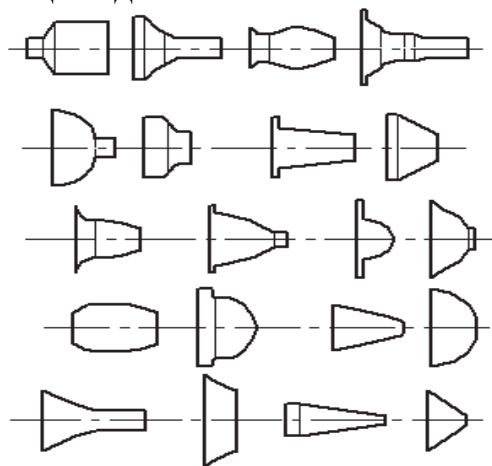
Деталі, що виготовляються ротаційної витяжкою
